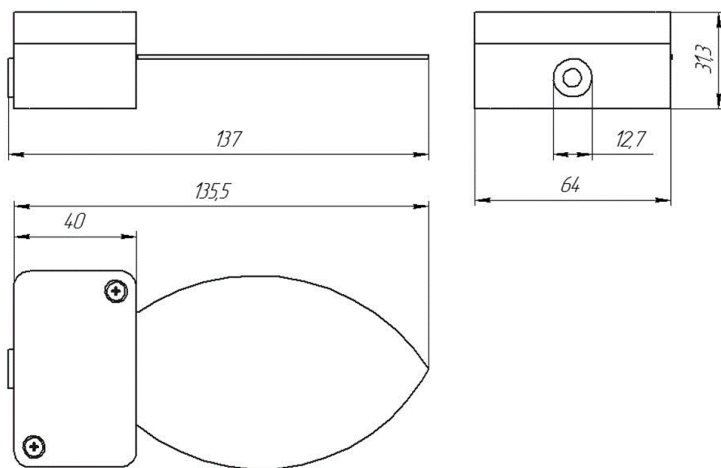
Габаритные размеры изделия «СОКОЛ-ДВЛ1».
